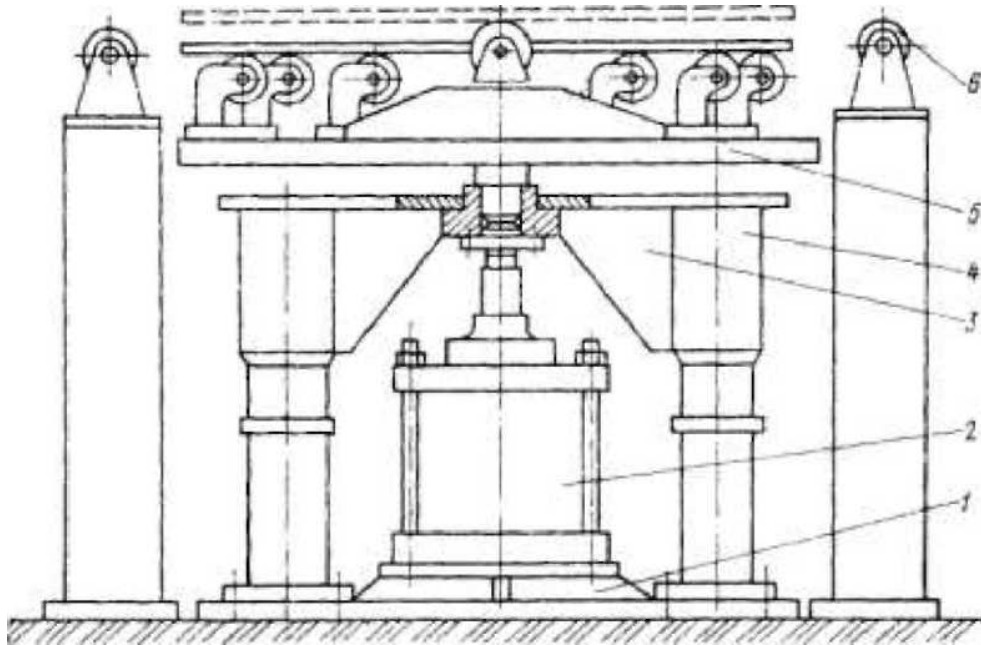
Подъёмно-поворотный стол: 1 – основание; 2 – пневматический подъёмник; 3 – основание стола; 4 – колонна направляющая; 5 – стол поворотный; 6 – ролик
